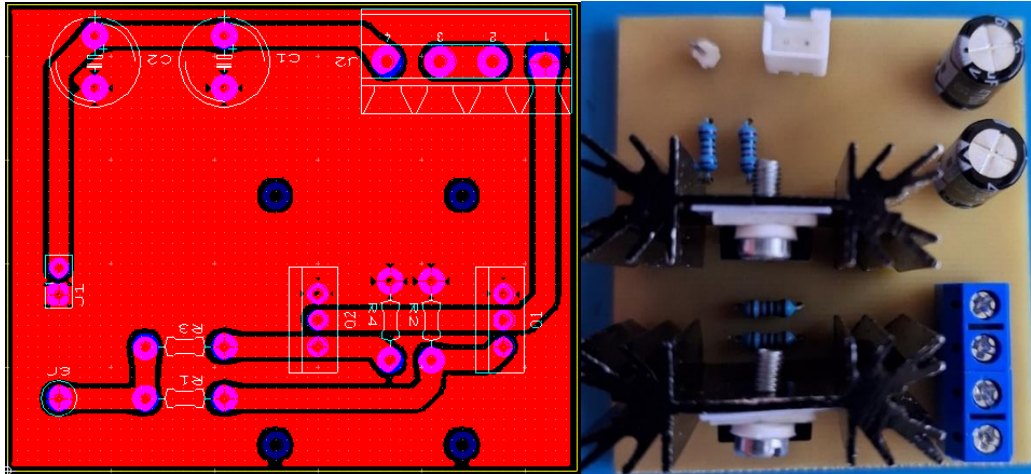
Diseño PCB del circuito de control de corriente mediante MOSFET
